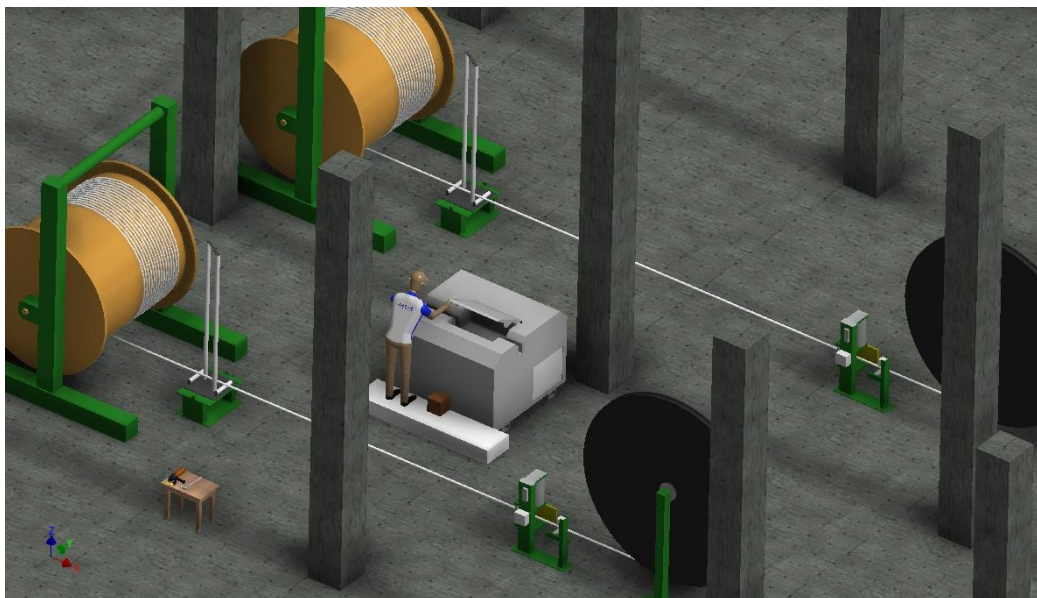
Configuração atual dos equipamentos utilizados na soldadura
